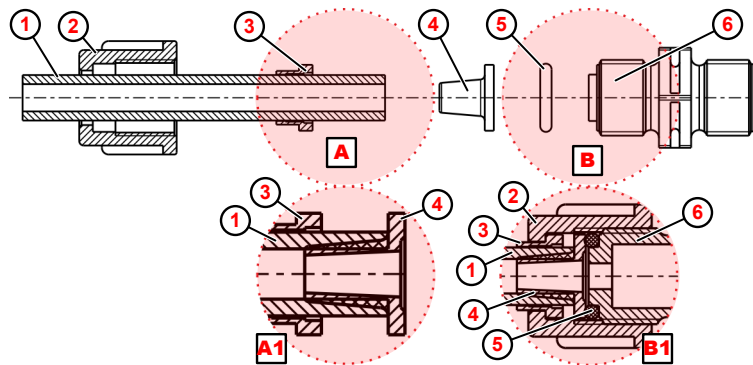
Rohr- Schlauchanschluss mit Kegelteil
